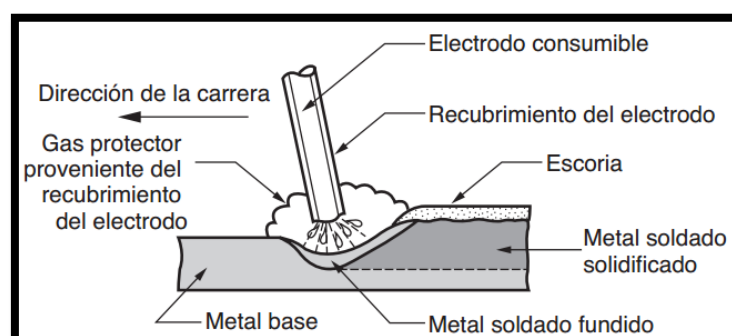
Soldadura de arco eléctrico y sus partes.
